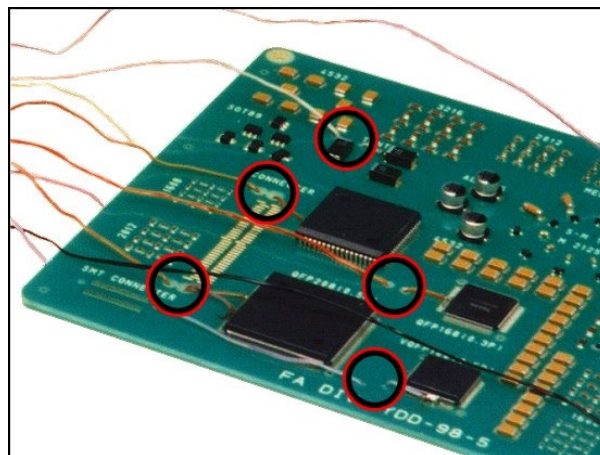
Fijación de un termopar a un PCB mediante soldadura
